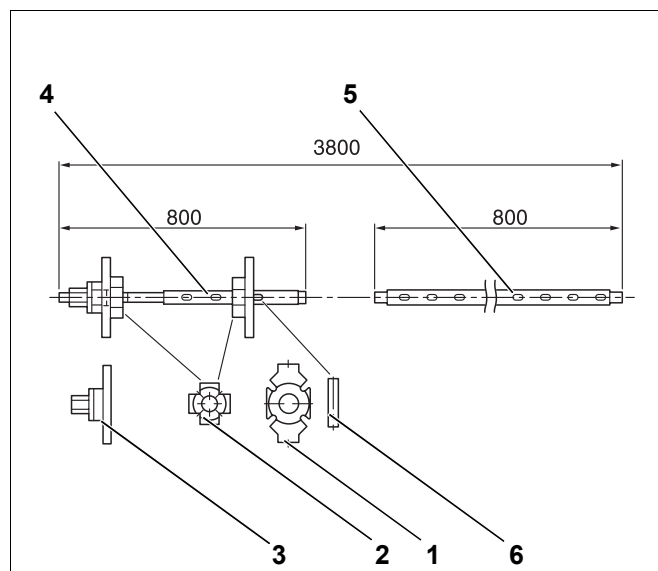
Strettoi di montaggio dimensioni 2.3 (misure in mm)
